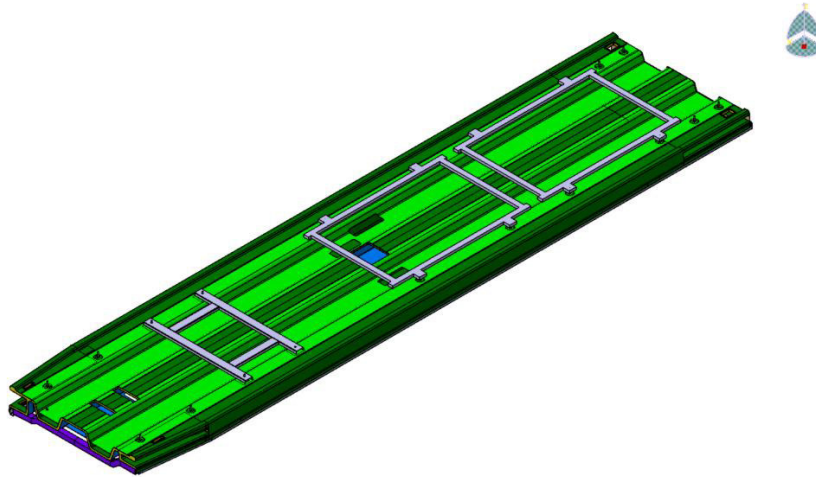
Finales Modell des Leichtbaudaches mit Träger für Dachgeräte
